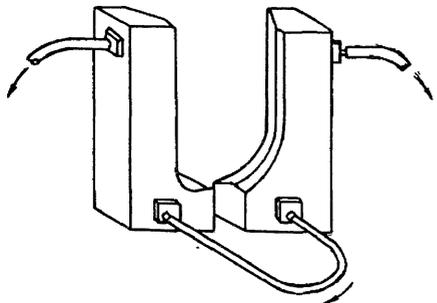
Общий вид охлаждаемых водой форм для ванны одноэлектродной сварки.
